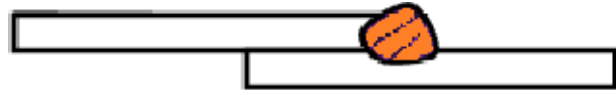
Soudage par recouvrement simple.
